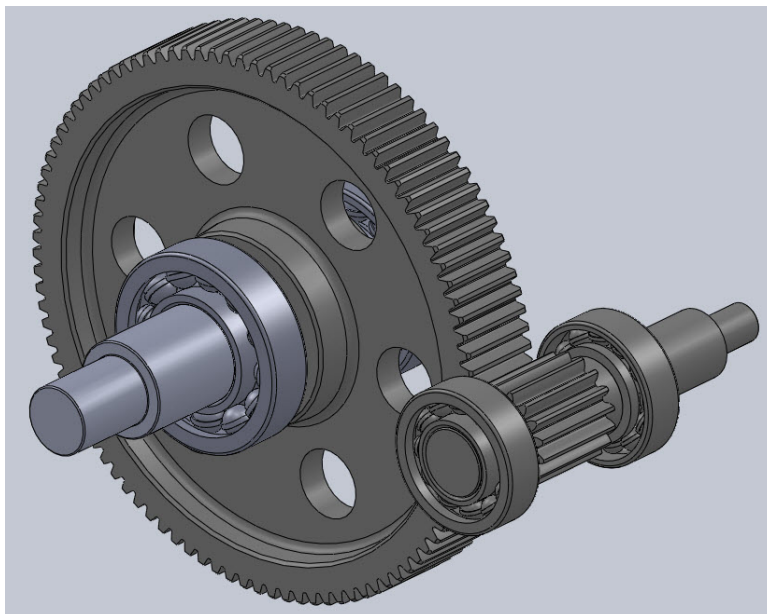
Зубчасте зачеплення. Вінець колеса і шестерня виконані у GearTrax
